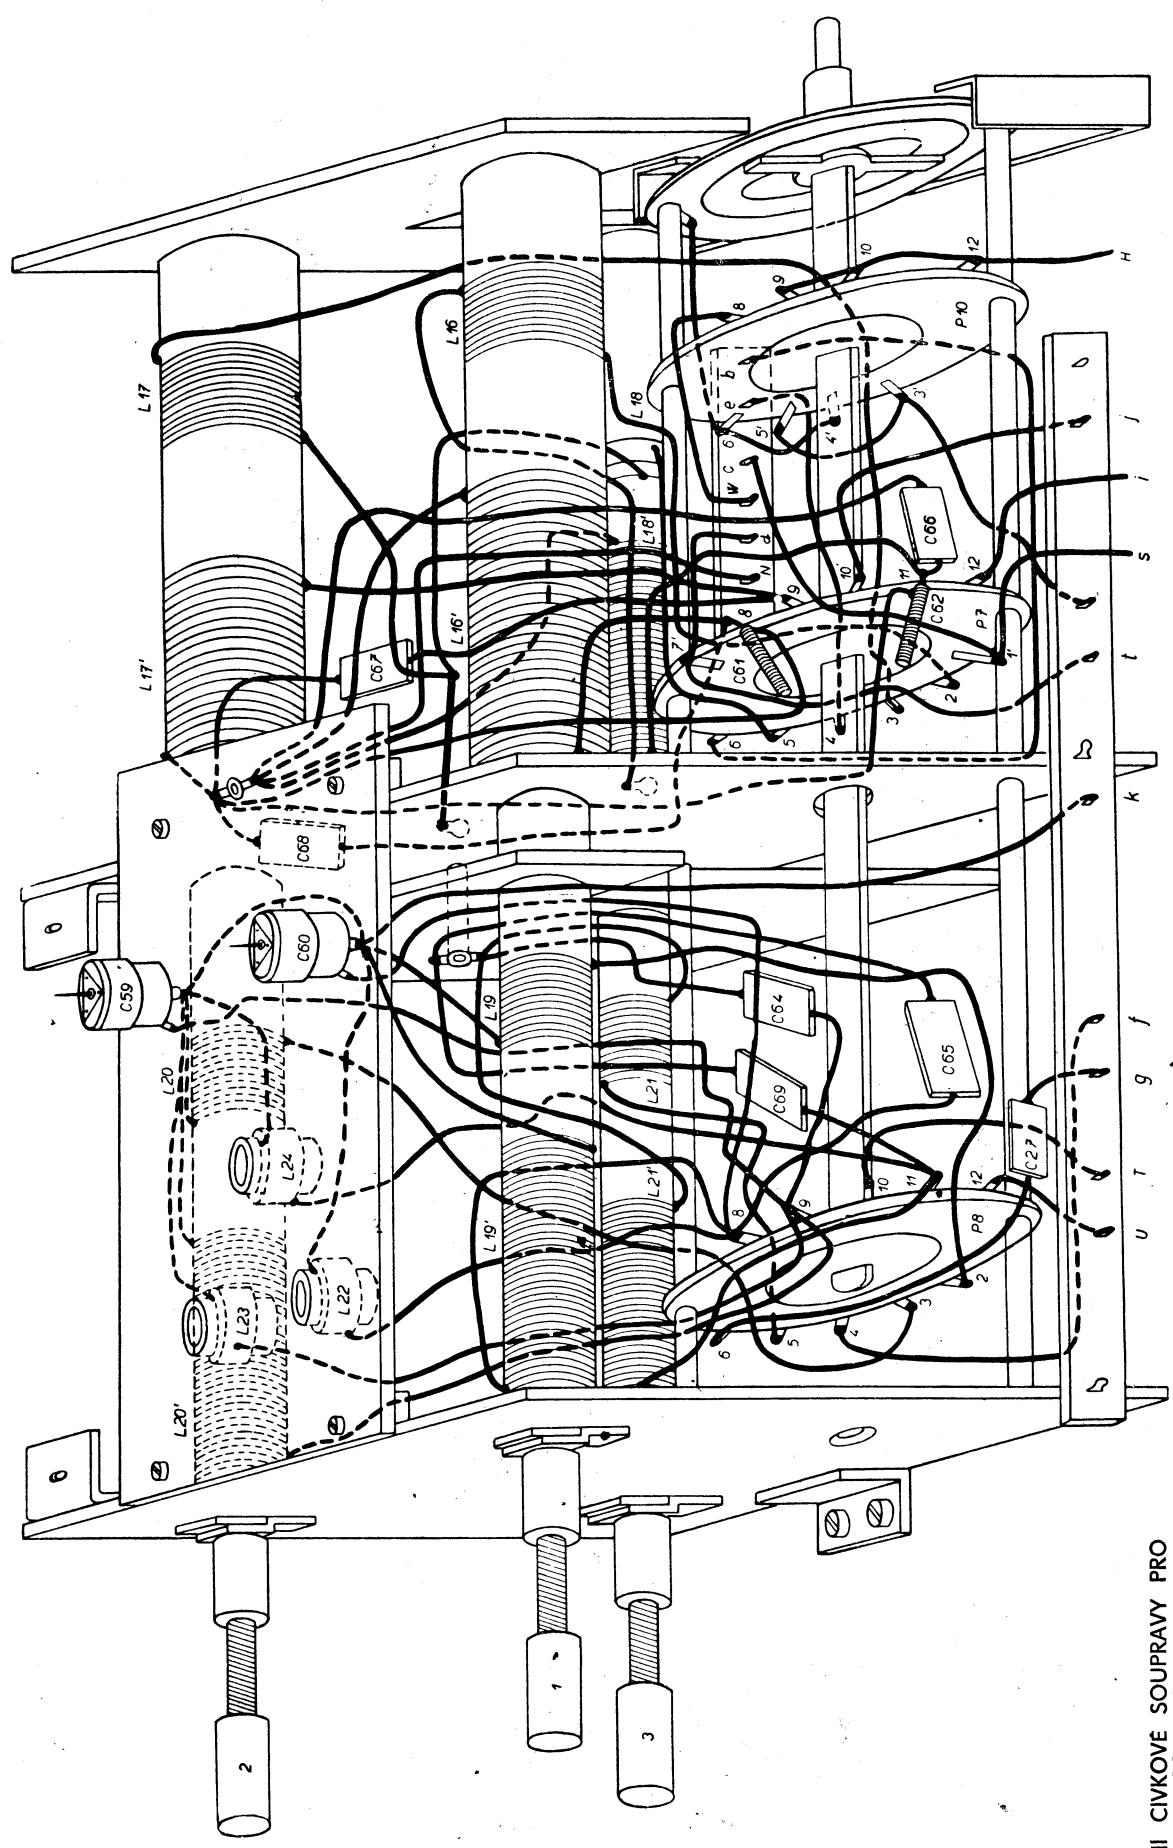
ZAPOJENÍ PRIJIMAČE NA CHASSIS.
